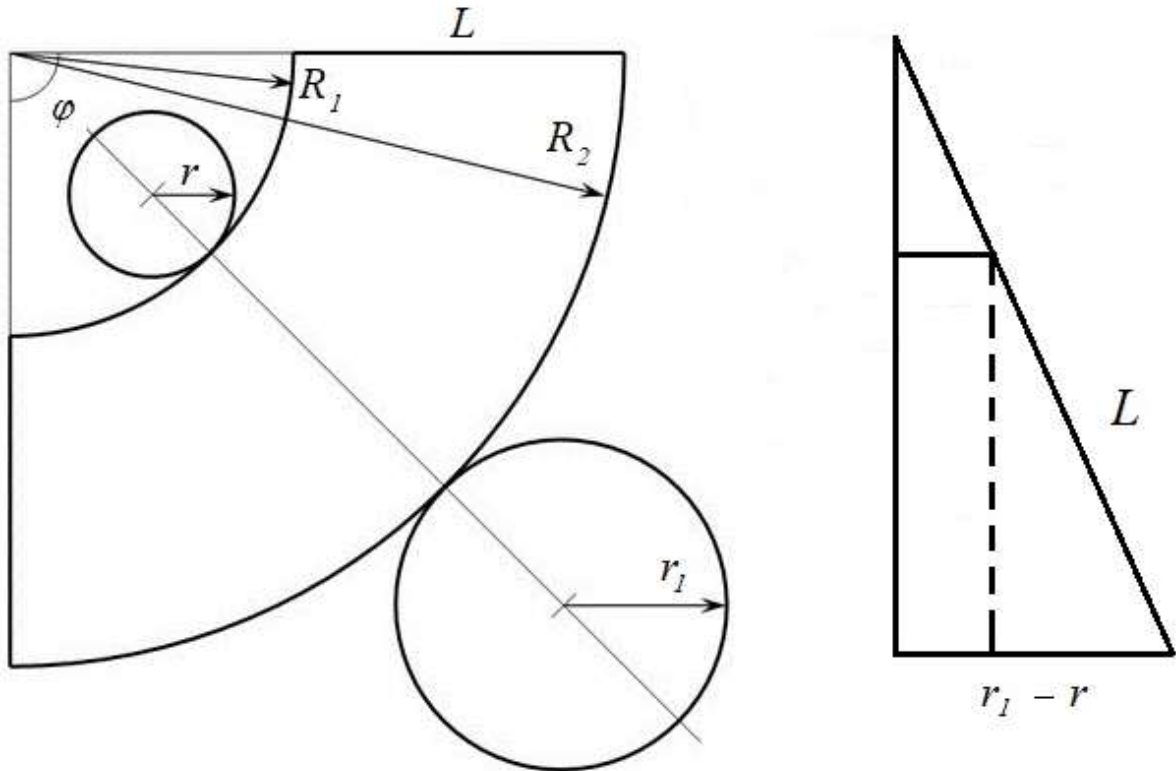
Розрахункова схема розгортки конуса світлорозподільвача
